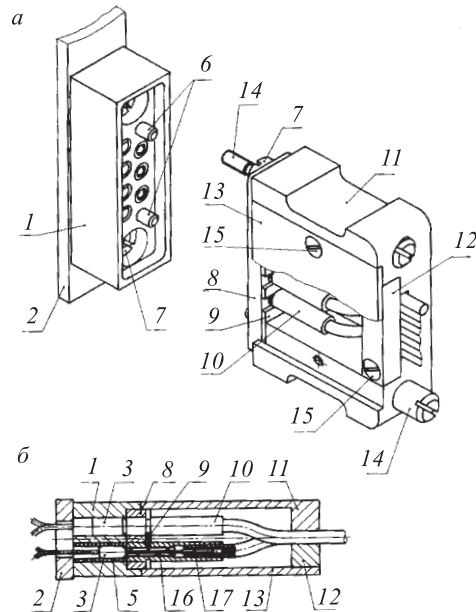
Многоконтактный оптический соединитель: *a* — разъем; *б* — разъем в разрезе; 1 — корпус (приборная часть); 2 — передняя панель модуля КАМАК; 3, 4 — оптические элементы; 5 — изолирующая втулка; 6 — направляющие штифты; 7 — узел крепления; 8 — юстировочная пластина; 9 — гребенка; 10 — наконечник; 11 — корпус (кабельная часть ОС); 12 — фиксатор ВОС; 13 — крышка; 14 — винт-фиксатор; 15 — элемент крепления; 16 — капилляр; 17 — оптическое волокно
